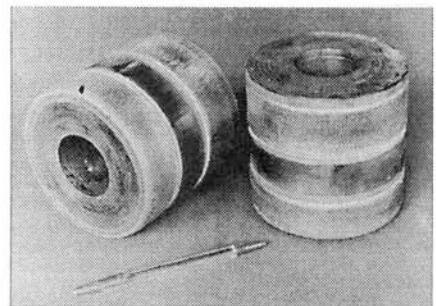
Наплавленный порошком из бронзы поршень гидроцилиндра
